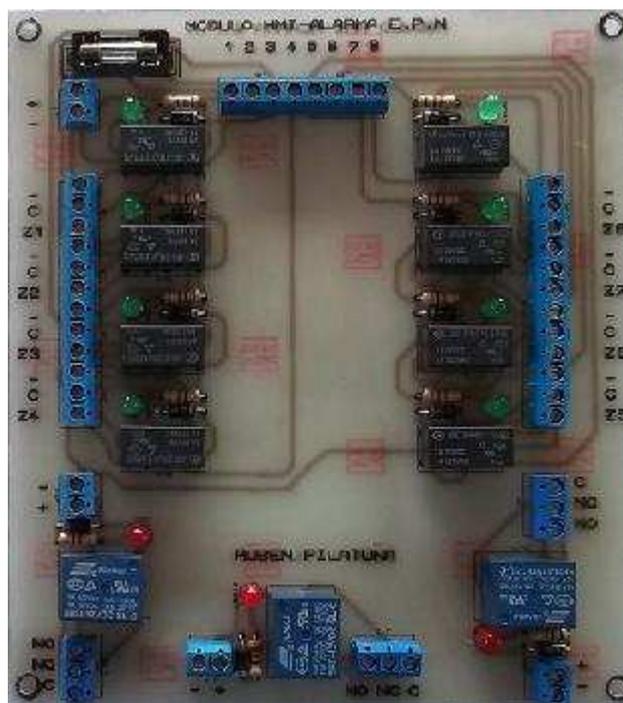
Placa módulo de acoplamiento vista frontal.
